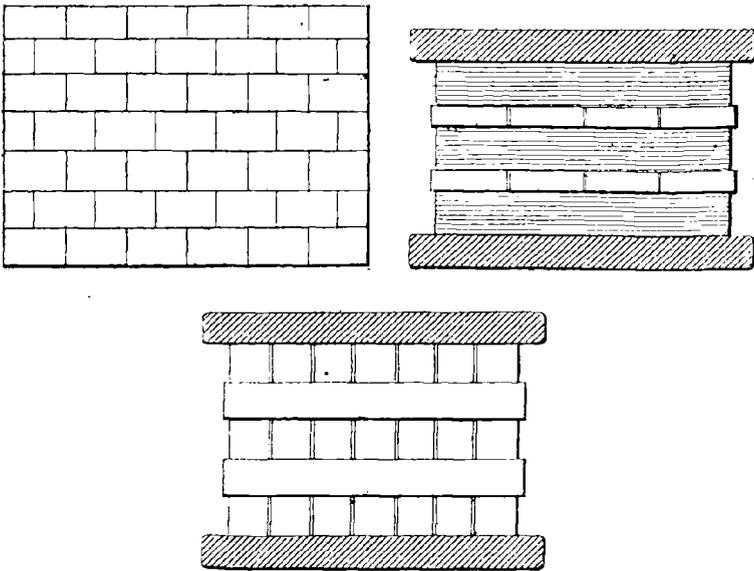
Paquets pour tôles en fer soudé.
